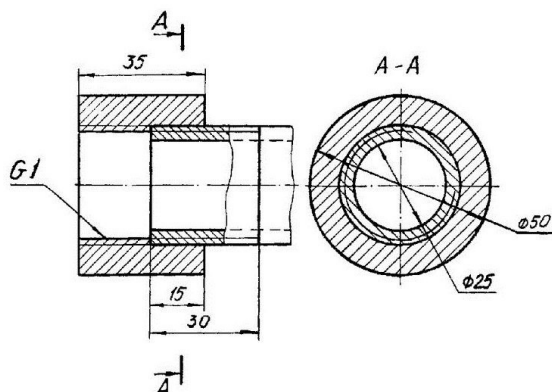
Образец задания. Трубное соединение двух деталей
